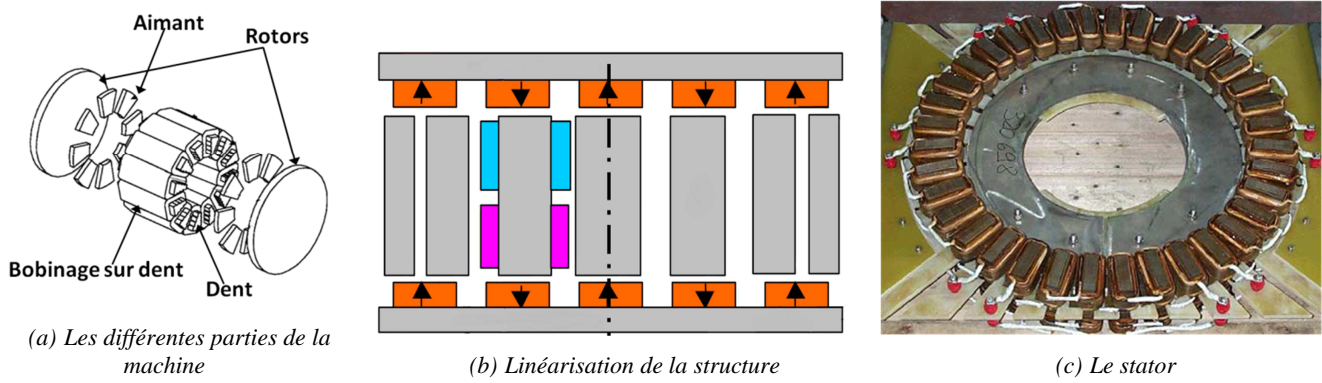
Structure d'une machine double rotor simple stator à bobinage concentré double couche [DiGe05]
